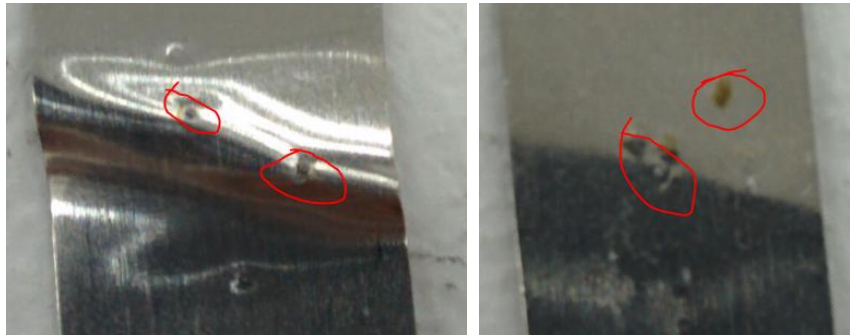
Detalle de test de soldadura incorrecto
